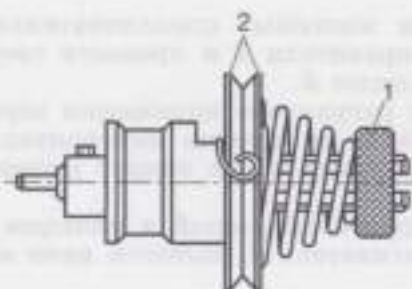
Регулятор натяжения верхней нитки машины 97-А класса:
